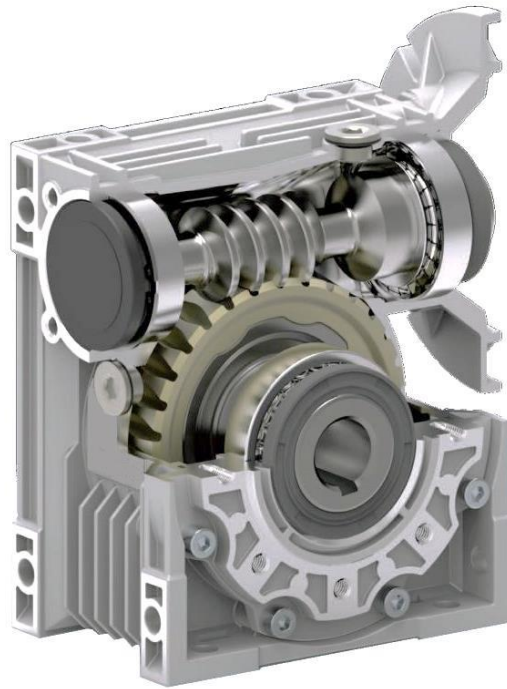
Редуктор черв'ячний з верхнім розташуванням черв'яка
